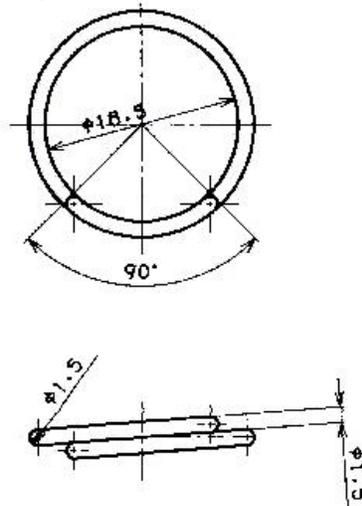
Formato e dimensões em mm do anel de brasagem.
